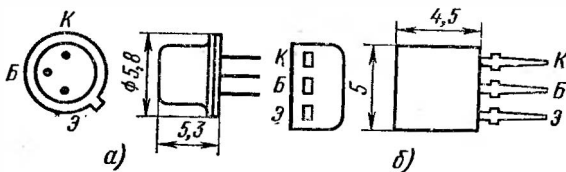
Цоколевка и габаритные размеры транзисторов:
